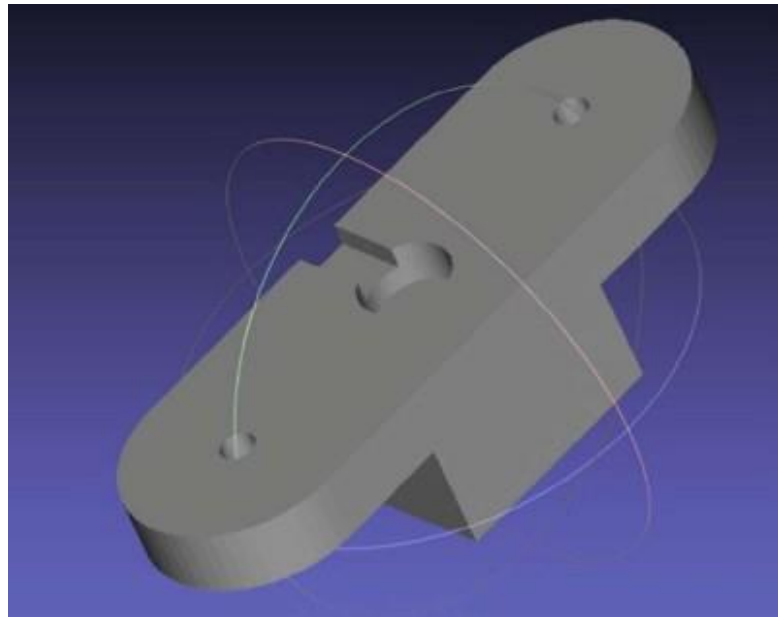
3D модель частини корпусу деталі типу Т-207
